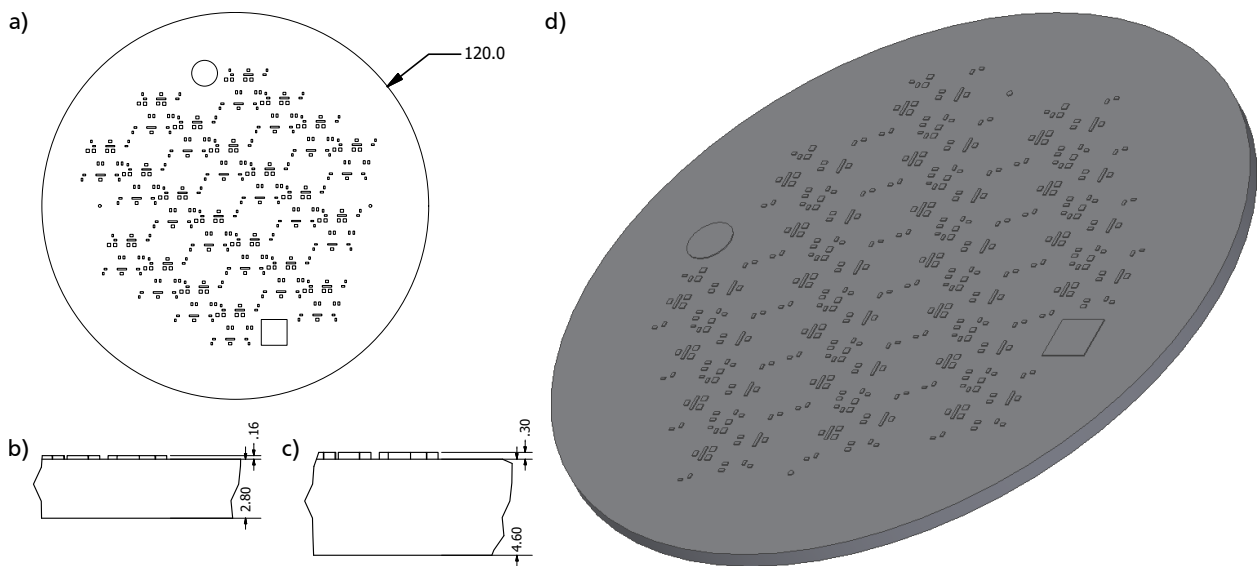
Verwendete Passformen zur Herstellung von Einzelaktoren: a) Draufsicht und Durchmesser beider Passformen; b) Schnittansicht der Aluminium-Passform; c) Schnittansicht der Teflon-Passform; d) CAD-Modell der Aluminium-Passform.
